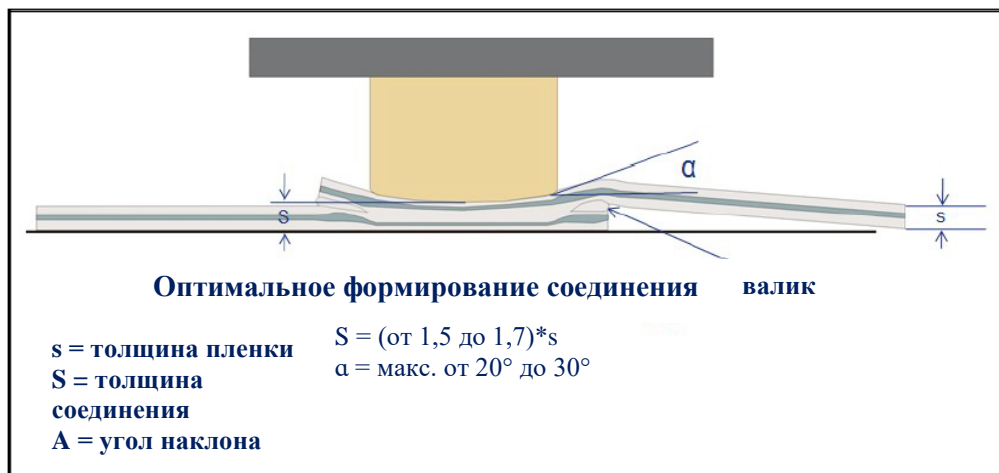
Схематическое изображение сварного соединения при ВЧ сварке многослойных пленок.
